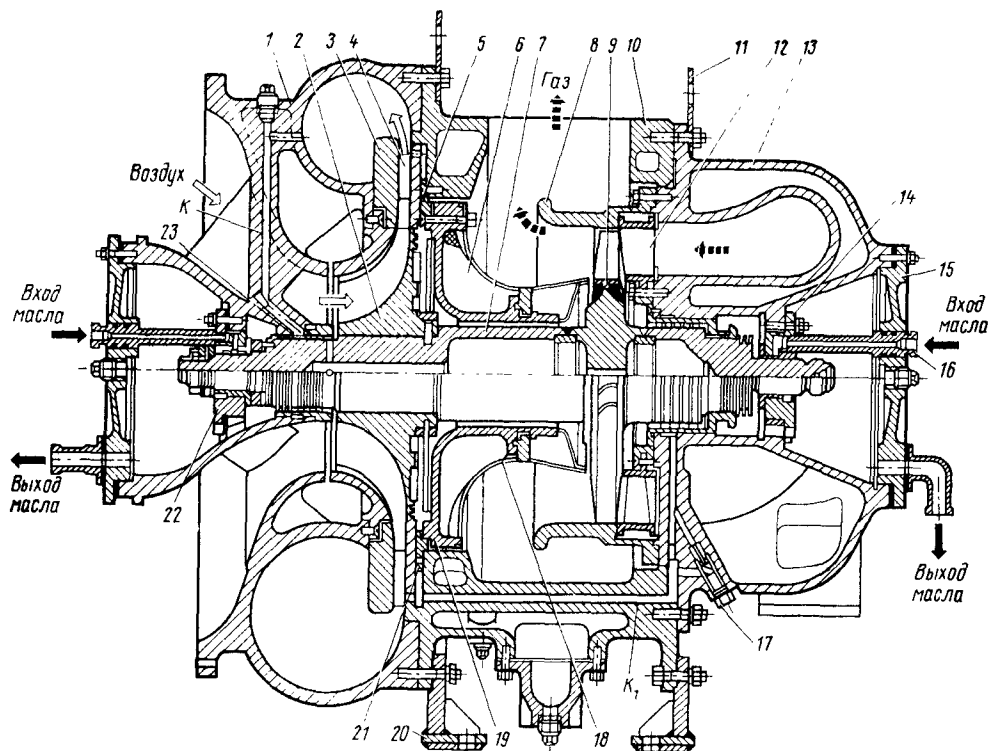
Продольный разрез турбокомпрессора типа ТК:
